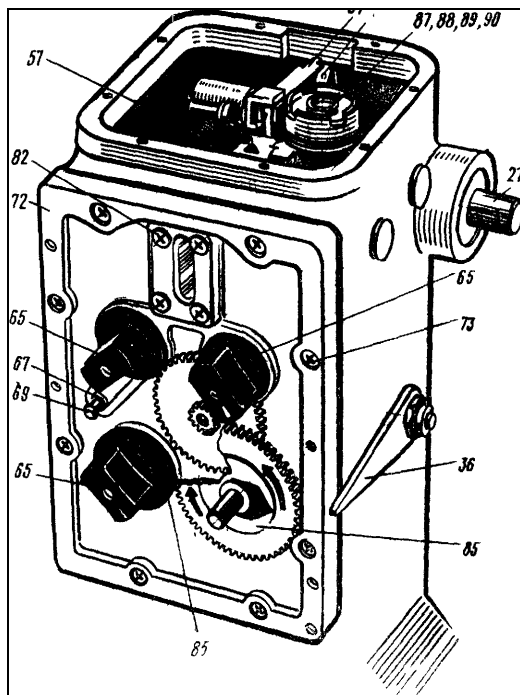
27— выходной вал; 36 — указатель настройки обратной связи; 57—натяжная пружина; 65— ручки управления; 67— пружинный тормоз; 69— палец пружинного тормоза; 72—панель; 73—винт крепления панели; 80 — прокладка указателя уровня масла; 81 — стекло указателя уровня масла; 82—винт; 85— указатели частоты вращения и ограничения нагрузки; 87— крышка фрикционной муфты; 90—корпус фрикционной муфты; 95—палец серьги; 97—рычаг регулирования неравномерности
